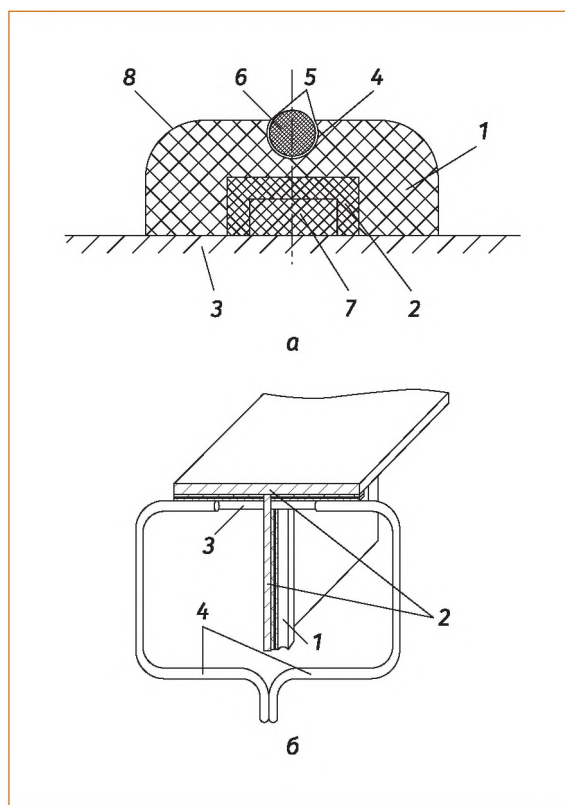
Заряд ударно-волновой резки (а): 1 – ВВ «Эластит-15»; 2 – инертная вставка; 3 – преграда; 4 – канавка; 5 – закраины для фиксации детонатора и ДШ; 6 – ДШ; 7 – виниловый магнит; 8 – скругления в краевых частях. Вариант крепления ЗУВР на конструкции (б): 1 – плоскость крепления; 2 – металлоконструкция; 3 – ЗУВР; 4 – ДШ
